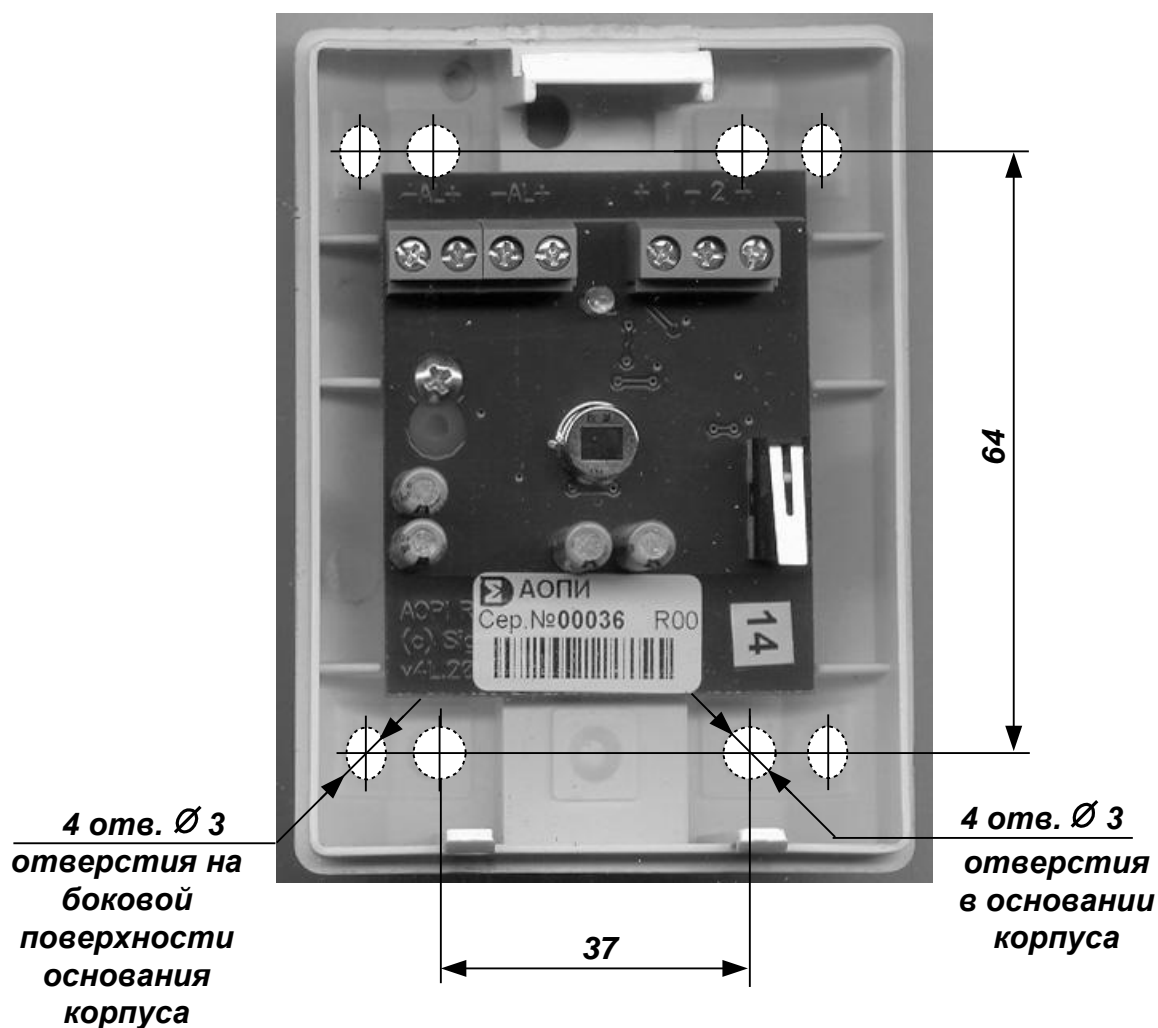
Присоединительные размеры корпуса АОПИ
